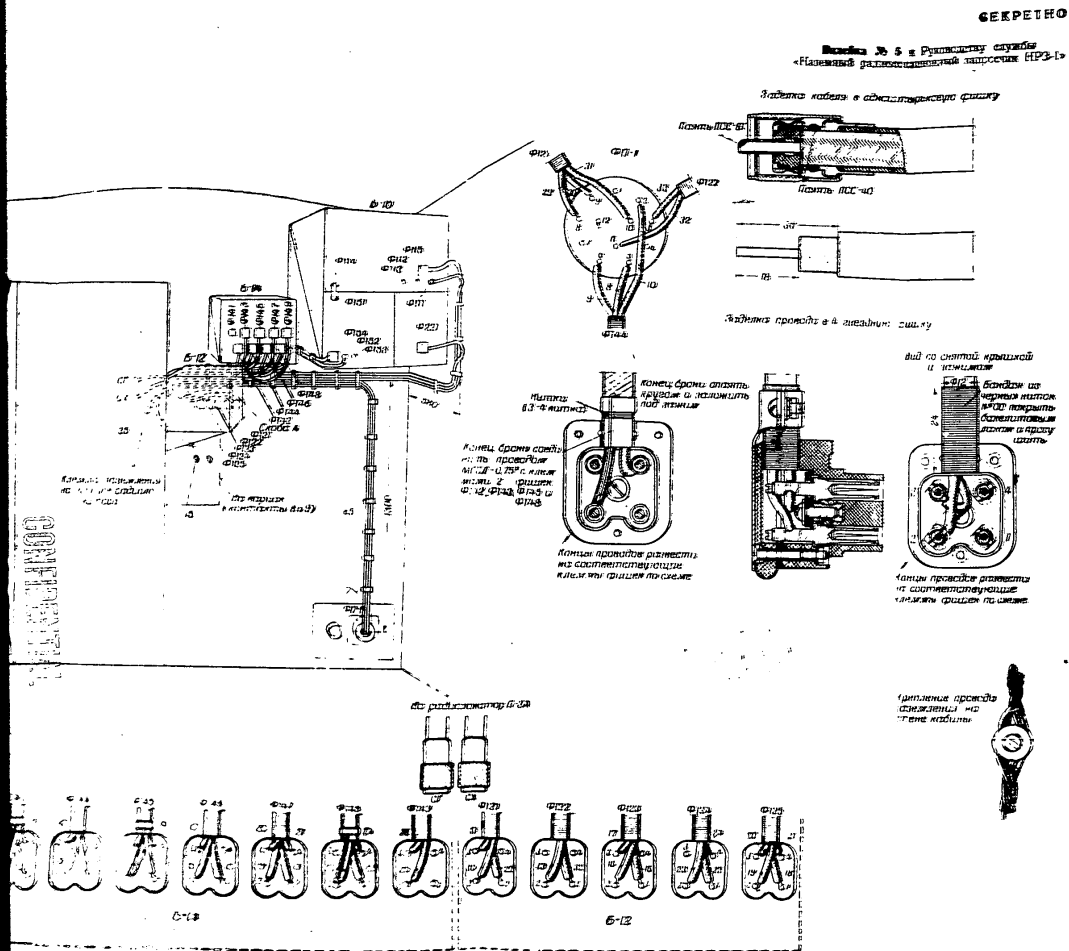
Схема монтажа кабеля межкомнатной связи с антенной НРЗ-1
